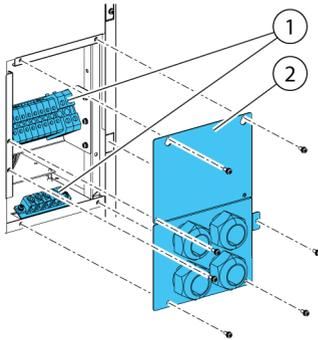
Ubicazione della piastra passacavi e dei connettori sui telai standard e modello C da 15-20 kW
